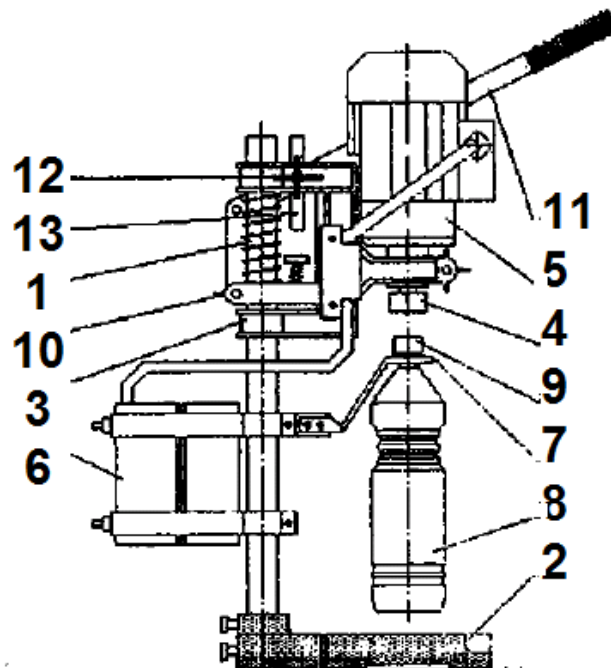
Напівавтоматичний пристрій закупорювання пляшок пробками з різью
